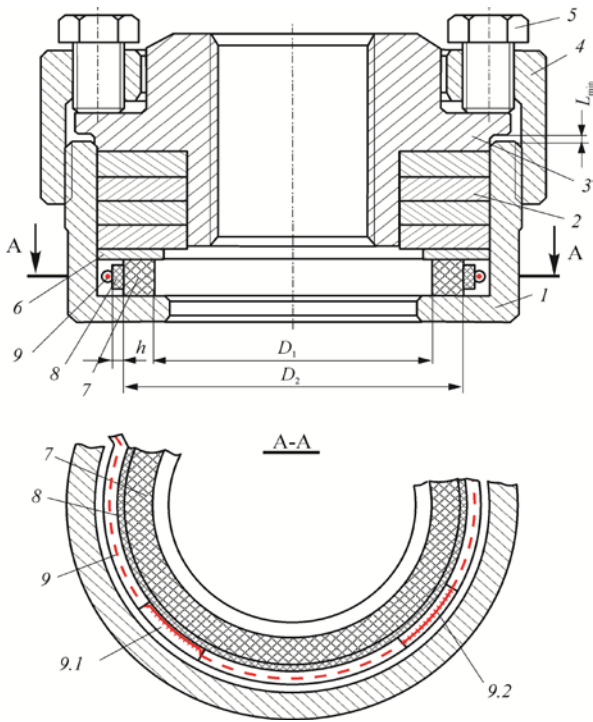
Конструктивна схема СА: 1 — внутрішній стакан; 2 — тарілчасті пружини; 3 — гайка; 4 — зовнішній стакан (корпус); 5 — відтискні болти; 6 — натискне кільце; 7 — кільцевий пружний фібергласовий силосприймальний елемент; 8 — кільцевий пружний вимірювальний фібергласовий елемент; 9 — оптичне волокно; 9.1 — вимірювальна ґратка Бреґа (ВБГ); 9.2 — термокомпенсаційна ВБГ
